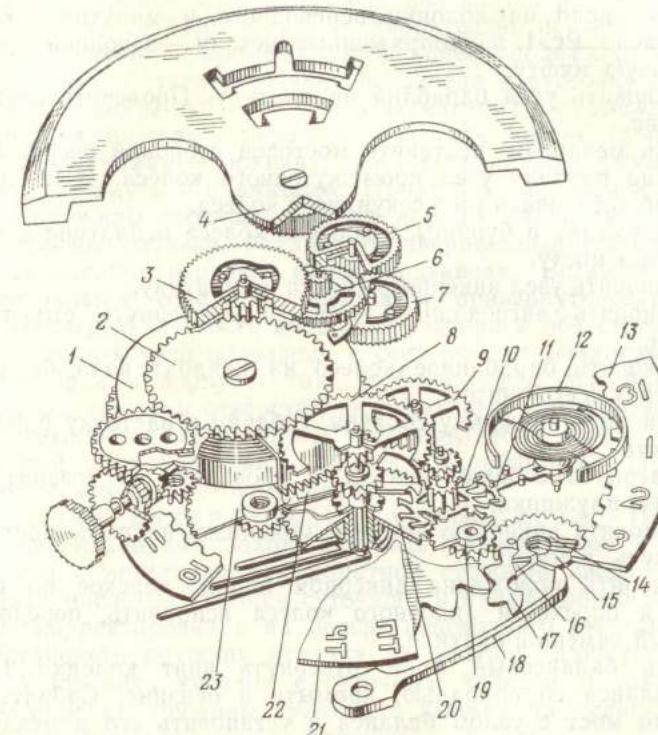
Кинематическая схема часов «Ракета» 2627:
